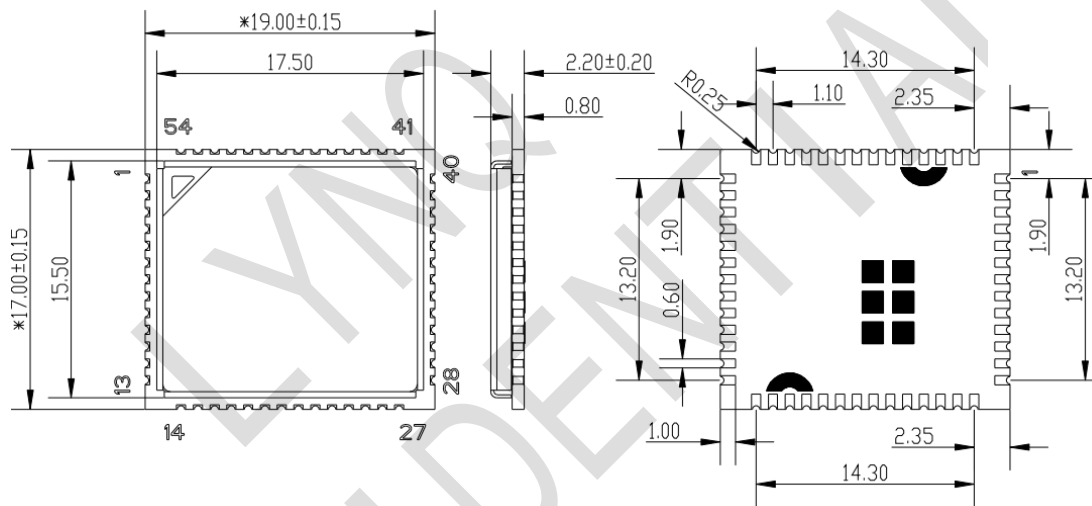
L216 俯视图、侧视图、底视图结构尺寸 (mm)
